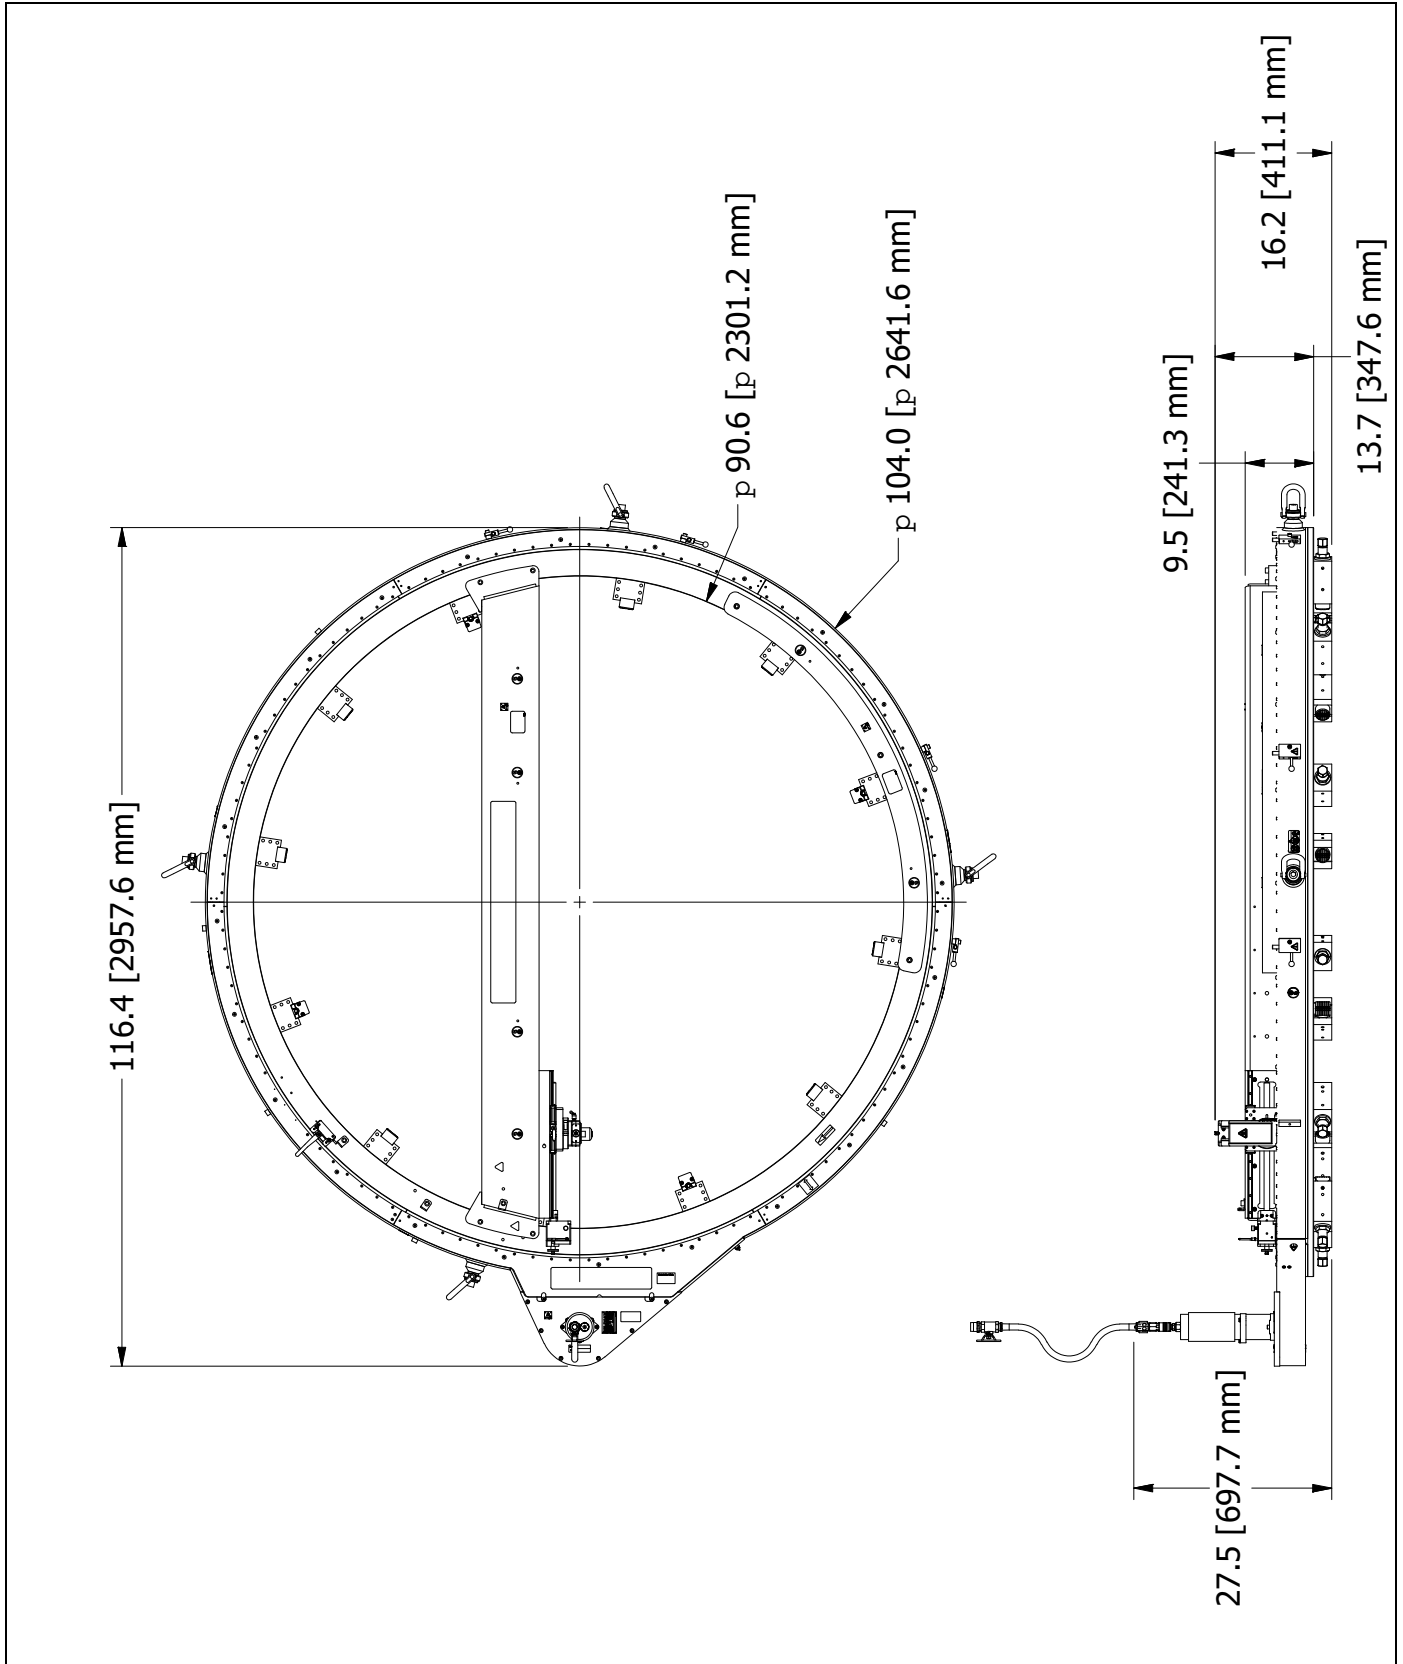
DIMENSIONES DE ODF90 SPEED FACER (N/P 94780)
